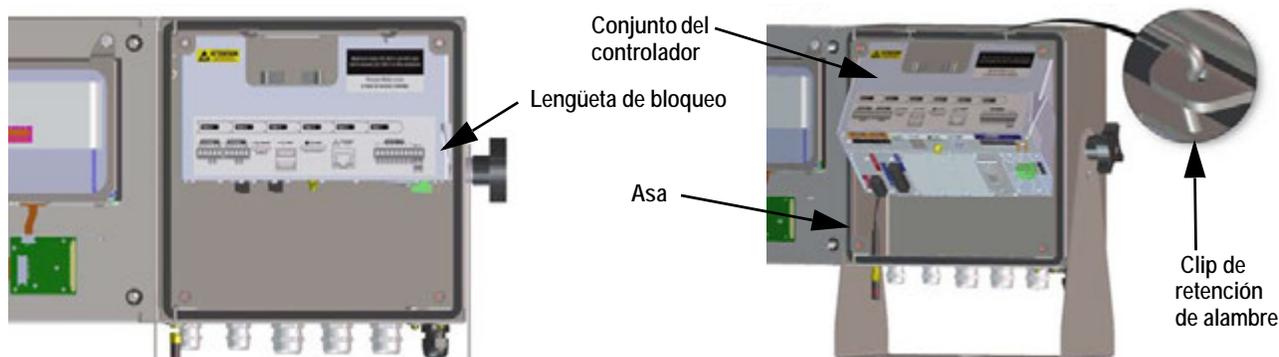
Extracción del conjunto de la CPU – Universal
